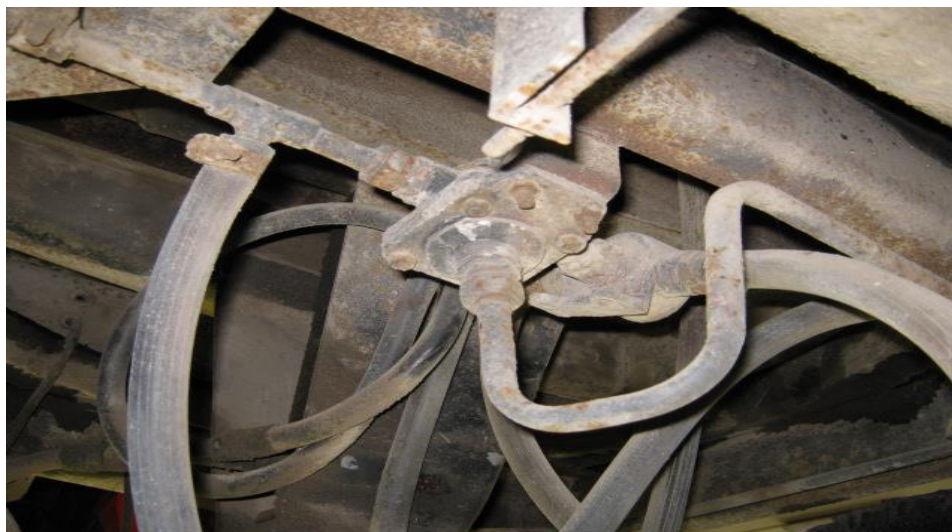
Koroze brzdových trubiček (vlastní foto)
